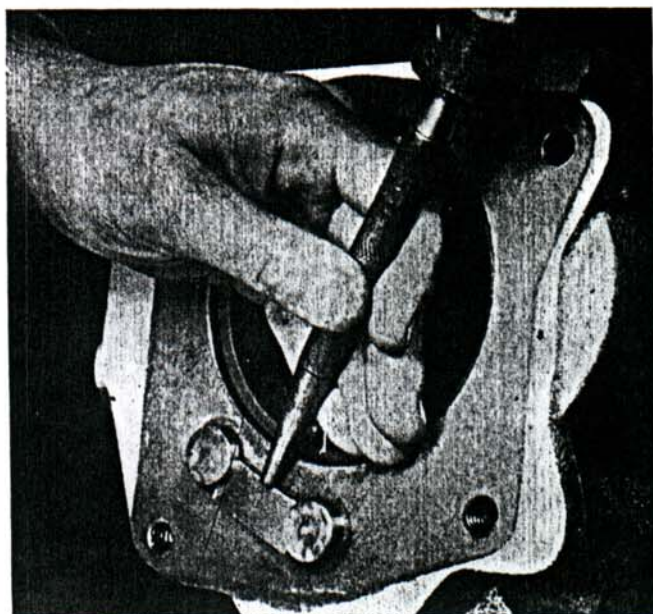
Extrayendo la placa traba, de los ejes del cuádruple y del engranaje libre de marcha atrás.
